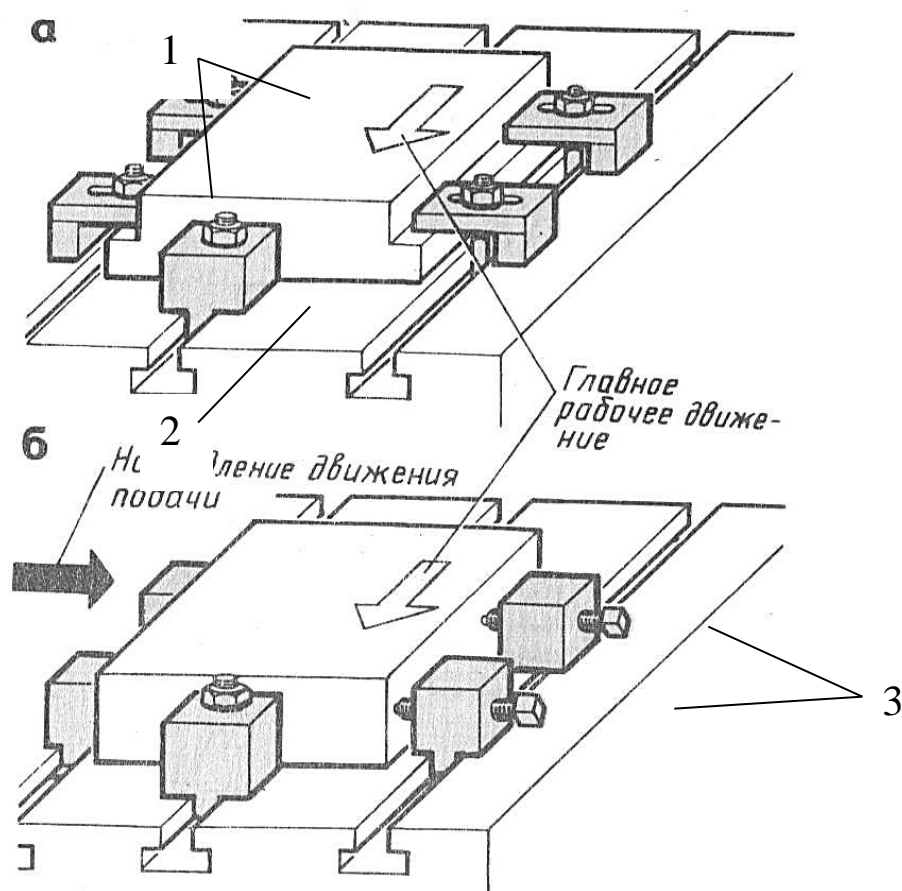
Примеры закрепления заготовок: 1- прихваты; 2 - упор, 3 – прижим винтовой
